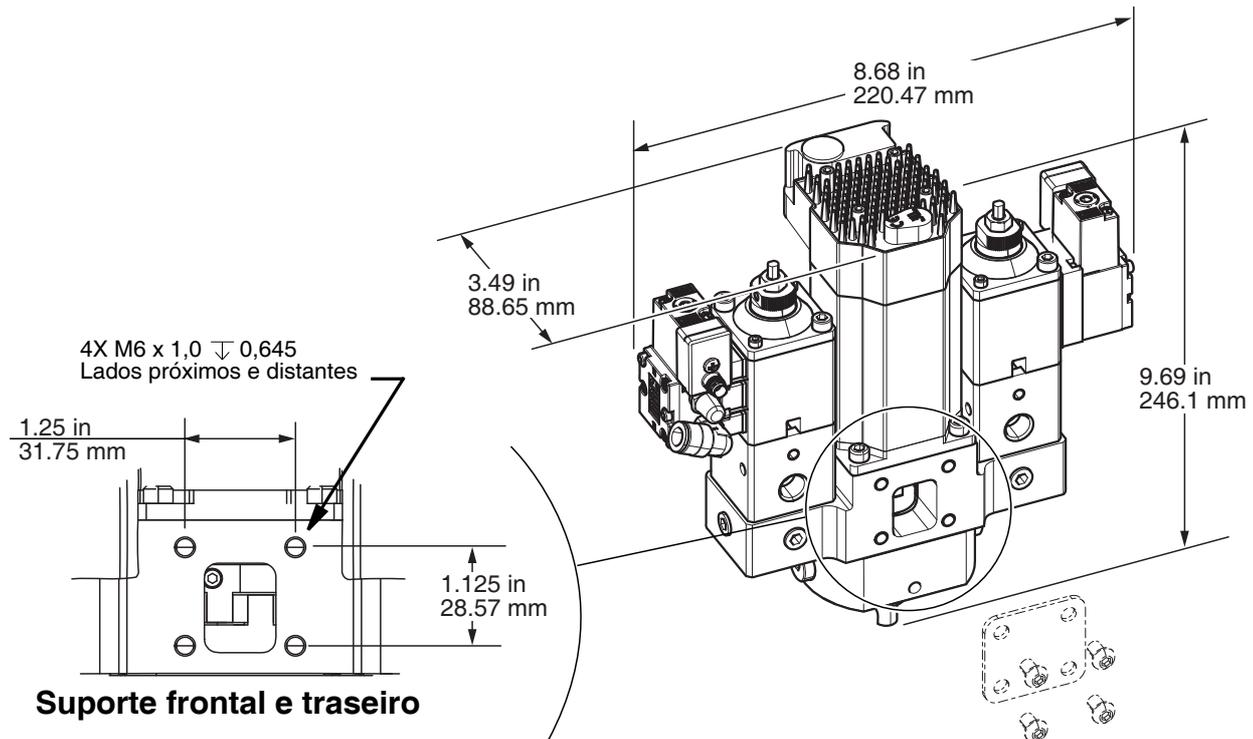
Dimensões da Válvula de Mistura Dinâmica Voltex
